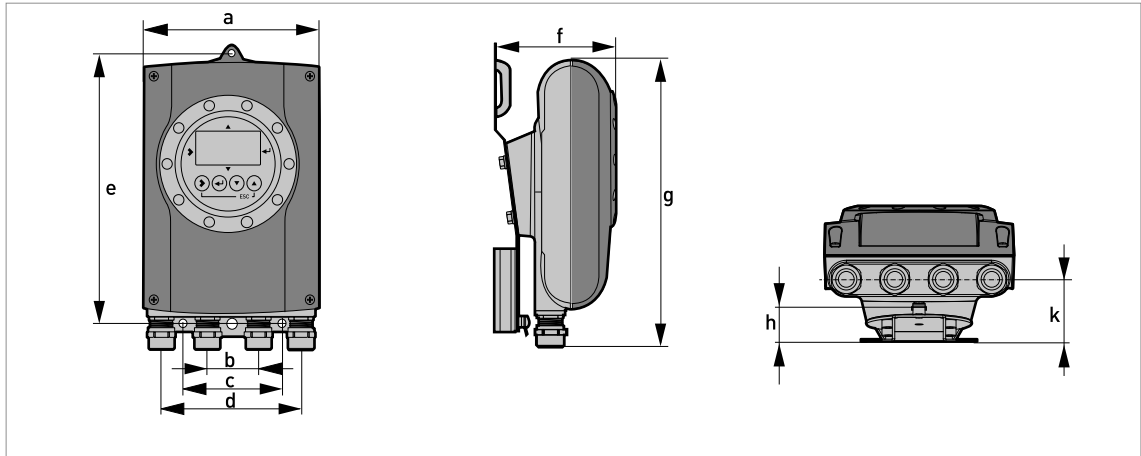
Габаритные размеры устройства раздельного исполнения
